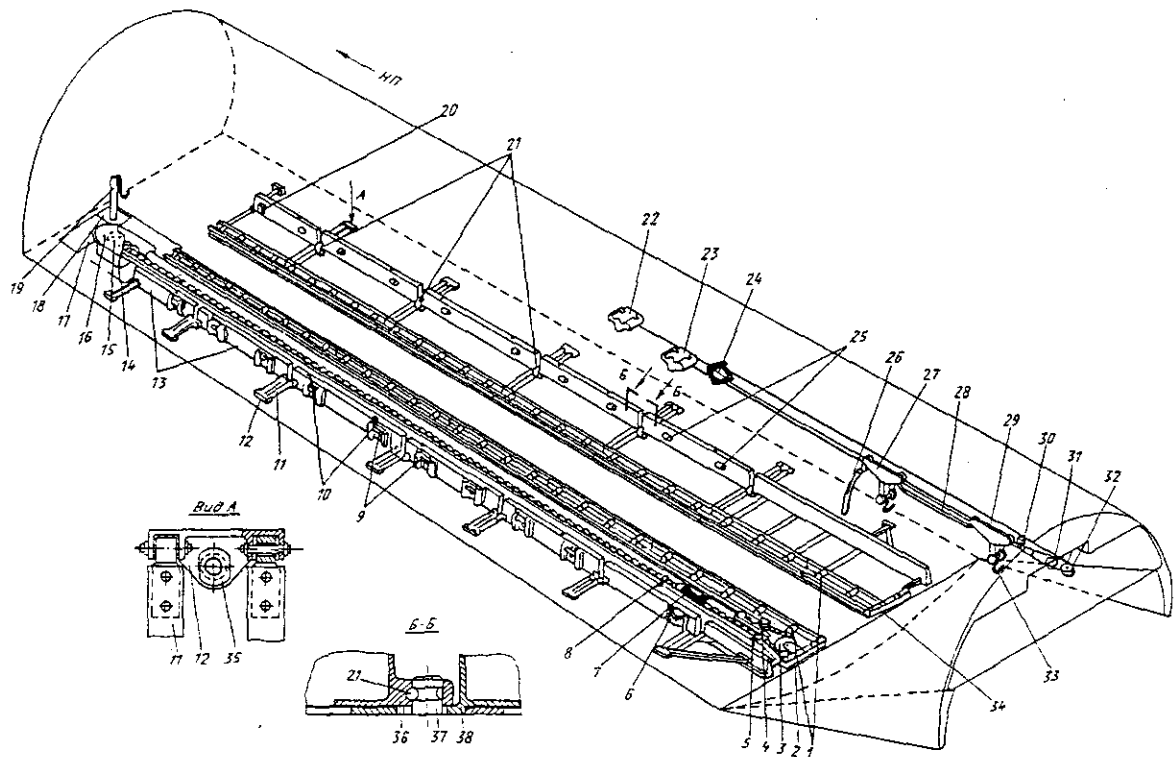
Грузоподъемное устройство и напольное устройство перемещения и крепления поддонов:
